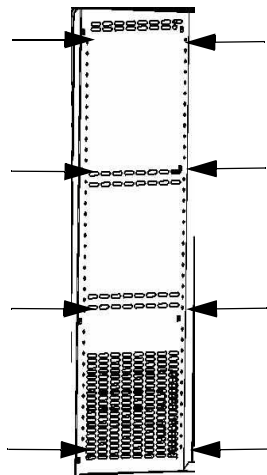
Remoción de los perfiles de soporte izquierdo y derecho
